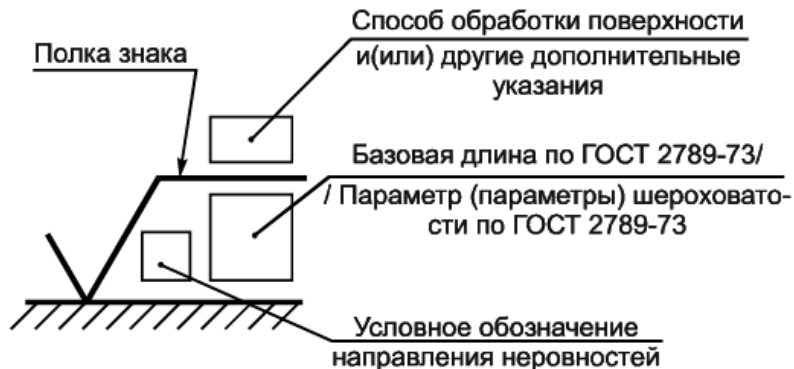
Структура обозначения параметра шероховатости на чертеже
